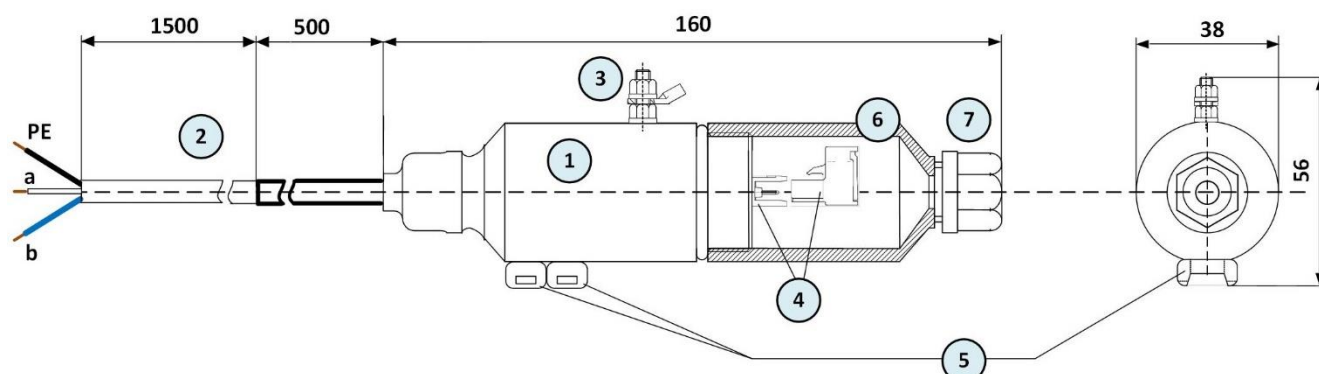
Конструкция и габаритные размеры АЗУ-Му (без креплений)
